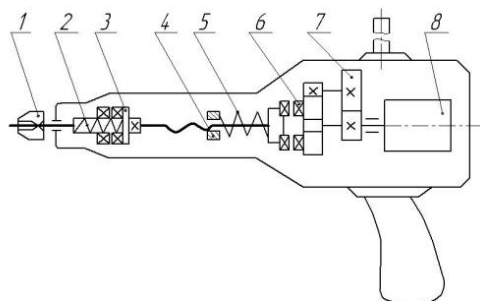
Електричний гайковерт: 1 – робочий наконечник; 2, 5 – пружини; 3, 6 – муфти; 4 – гайка; 7 – редуктор; 8 – двигун
